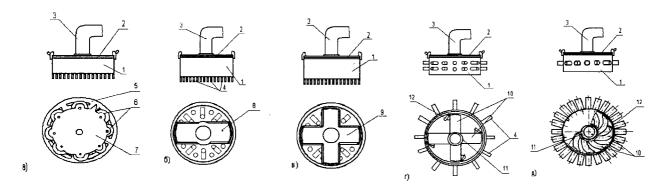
Распределительные головки с измельчительными аппаратами: 1 — корпус головки; 2 — крышка головки; 3 — нагнетательный патрубок; 4 — выливной штуцер; 5 — сменная противорежущая пластина с продолговатыми щелями; 6 — дисковые ножи; 7 — ротор; 8 — ротор с режущими кромками; 9 — крестообразный ротор с режущими кромками; 10 - патрубки ротора; 11—стакан ротора; 12 — нож
